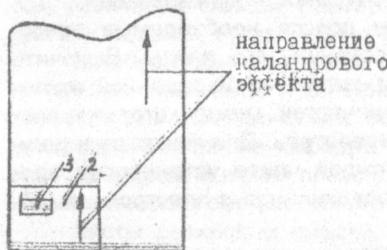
1 - Нист резиновой смеси; 2 - заготовка для вулканизации пластинки; 3 - бумажная этикетка
